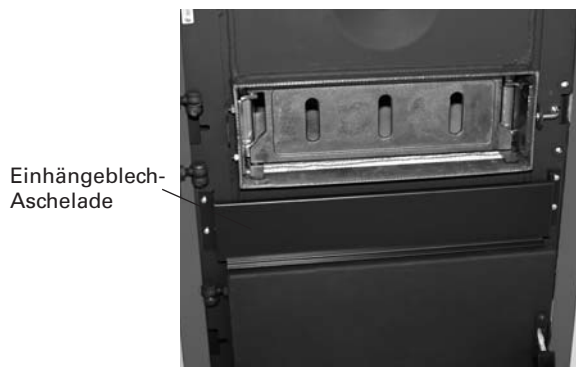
Einhängeblech-Aschelade mit 4 TT-Selbstschneide-Schrauben anschrauben
